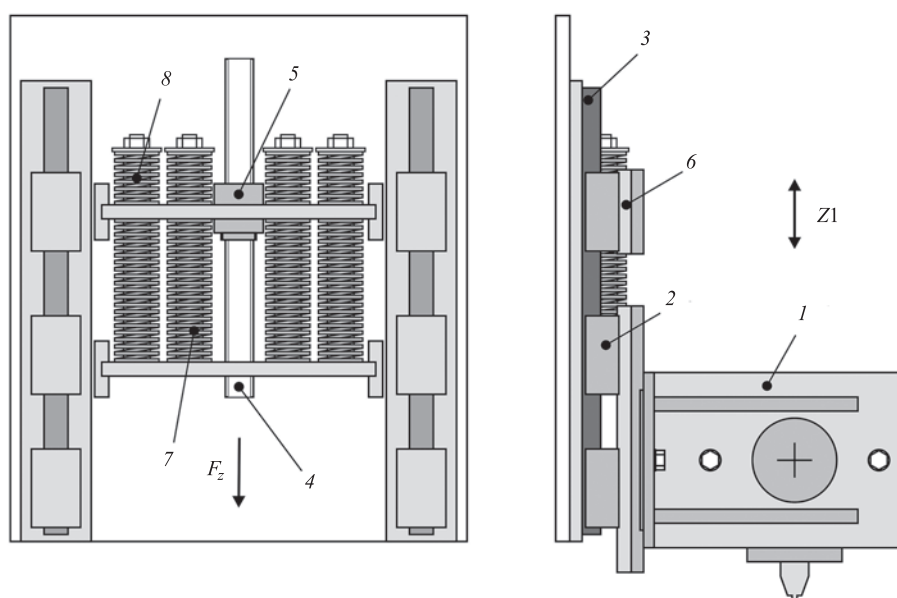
Схема генерации вертикальной силы на сварочном инструменте
